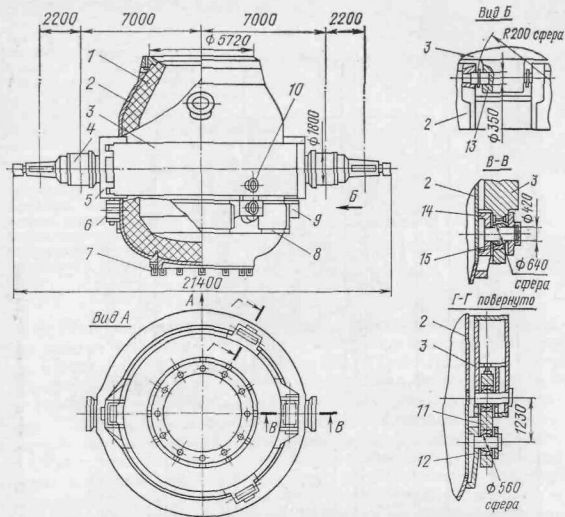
Корпус конвертера вместимостью 350—400 т с опорными кольцом и узлами крепления: 1 — шлем; 2 — корпус; 3 — опорное кольцо; 4 — цапфа; 5 — цапфовая плита; 6 — фиксированная опора; 7 — вставное днище; 8 — несущий пояс; 9 — упор; 10 — шарнирная подвеска; 11 — тяга подвески; 12 — шаровой шарнир подвески; 13 — сферическое подпятники упора; 14 — кронштейн фиксированной опоры; 15 — сферический шарнир опоры
